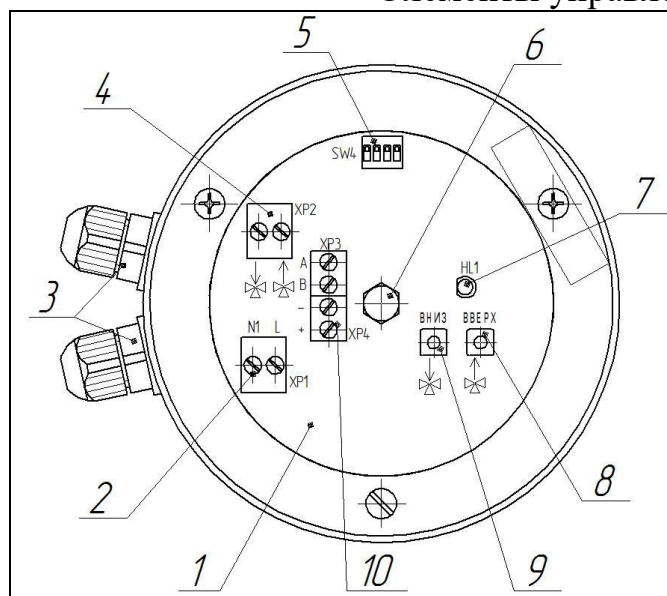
Привод ЭП-100 и ЭП-180 с открытой крышкой
